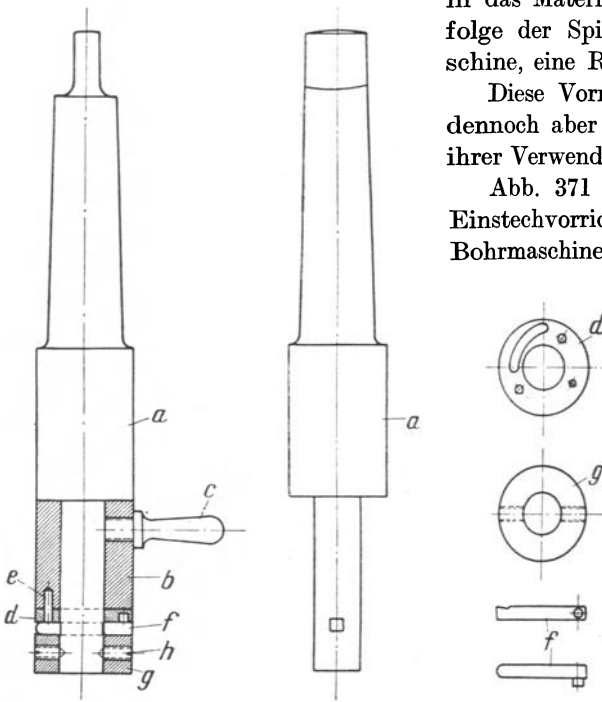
Nutenhinterstechvorrichtung mit Rundmesser für Bohrmaschinen.
